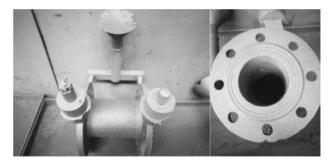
3D砂芯浇注后的铸件外观 Fig. 6 Casting appearance after pouring the 3D sand core
